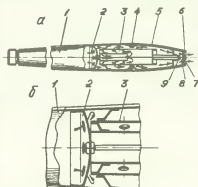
Правильное (а) и неправильное (б) положение акустического фильтра в глушителе: 1 — корпус глушителя; 2 — перегородка; 3 — акустический фильтр; 4 — асбестовая прокладка; 5 — хвостовик глушителя; 6 — решетка; 7 — гайка хвостовика; 8 — шпилька; 9 — гайка крепления фильтра.
